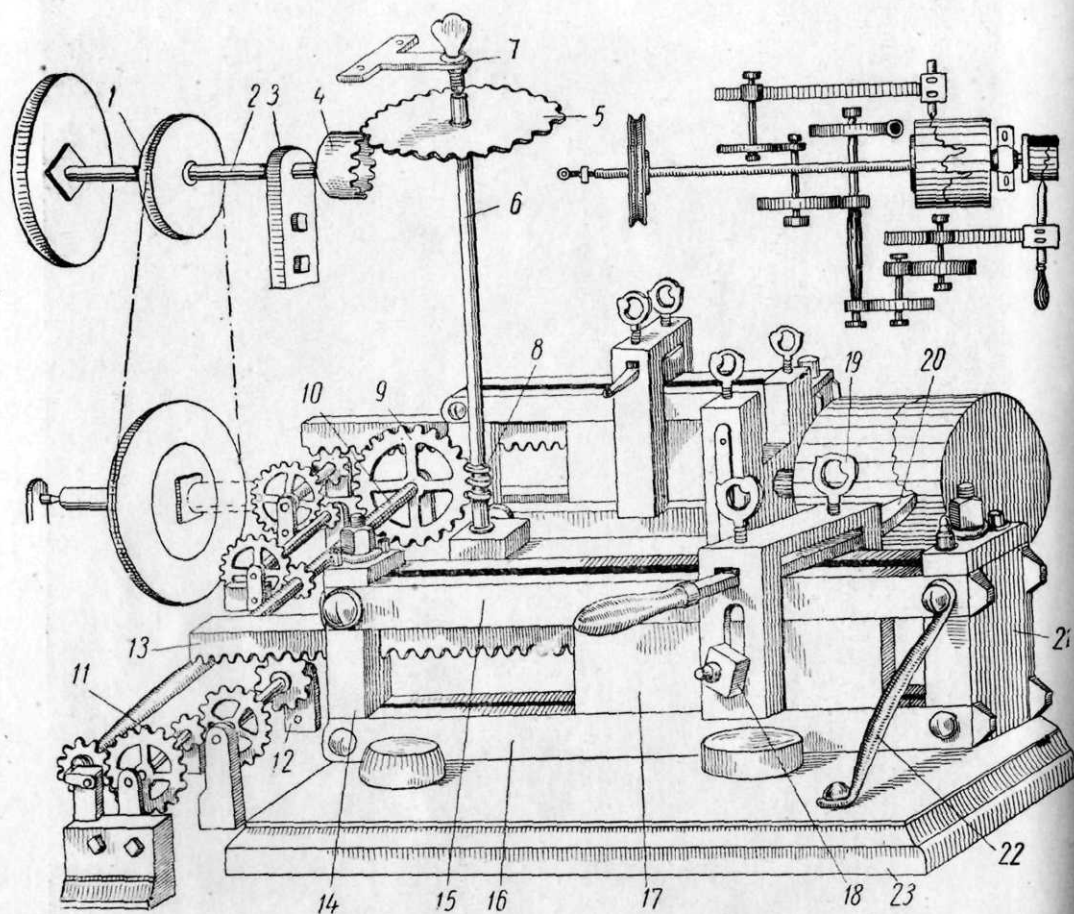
Ручной привод токарно-копировального станка Нартова 1712 г.
